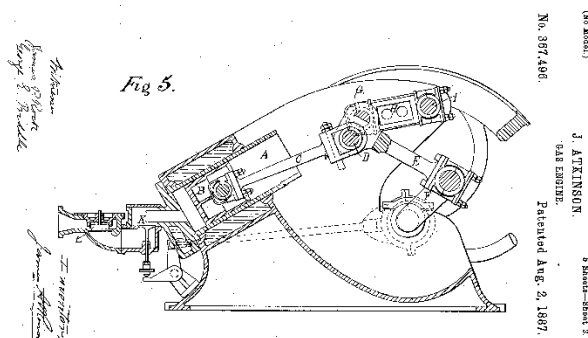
Motor de Atkinson (adaptado de [35])
